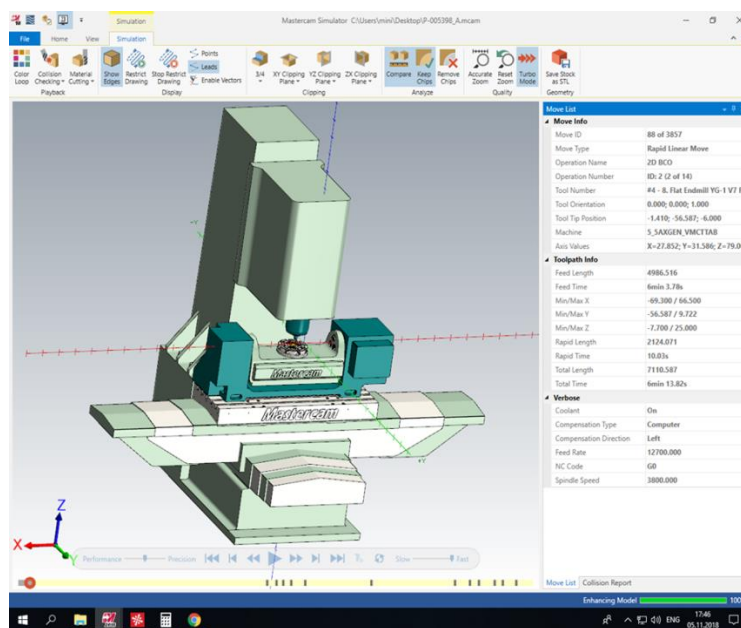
Обладнання для виготовлення корпусної деталі
